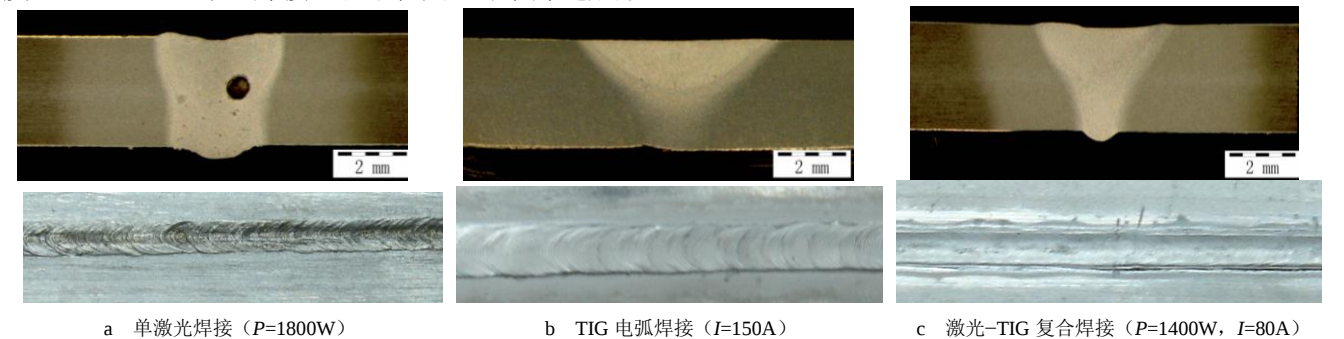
不同焊接方法的焊缝表面成形及其横截面（*v*=1m/min）
